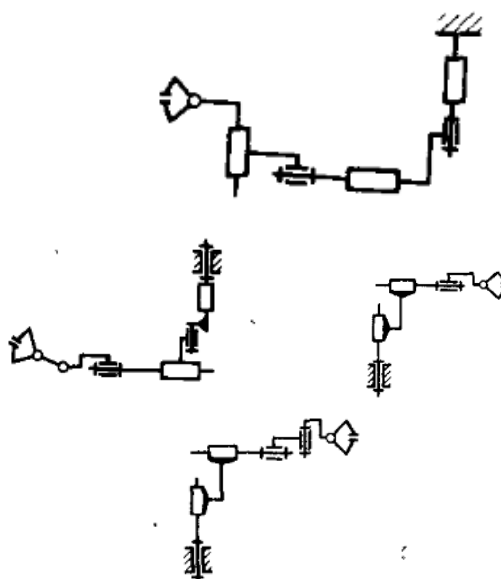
Кинематические схемы роботизированных устройств, работающих в полярно-цилиндрической системе координат [5]
